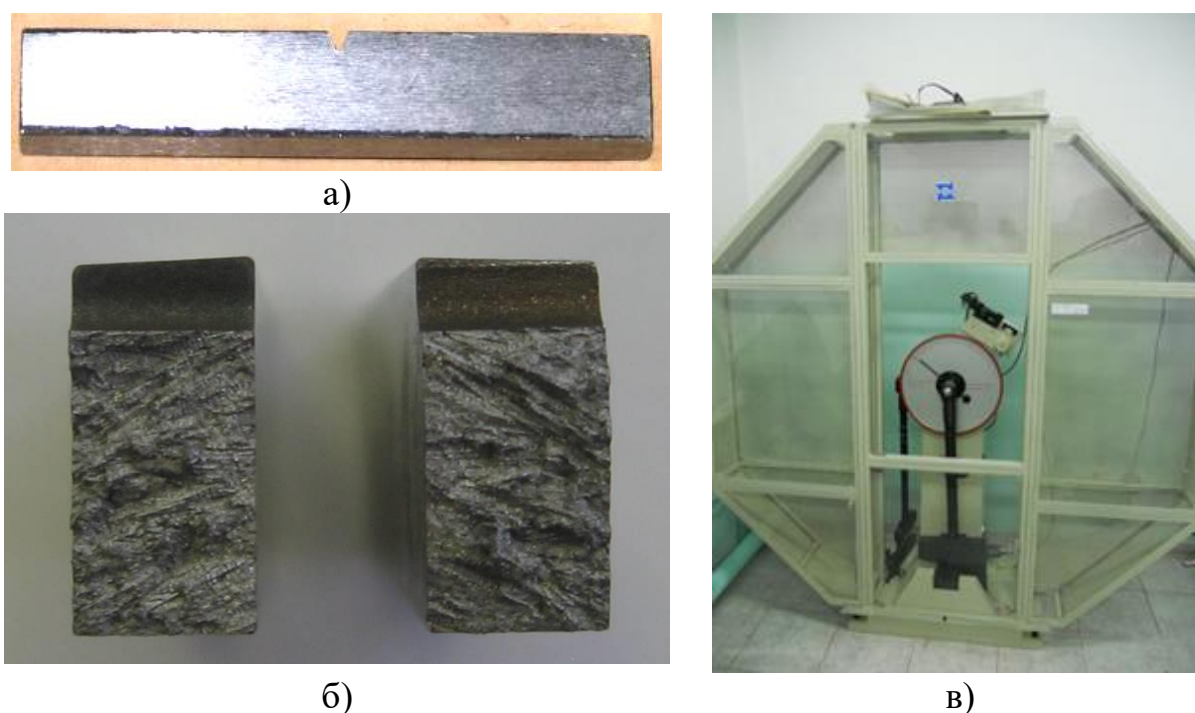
Вид образца до испытаний (а); вид изломов после испытаний (б); маятниковый копер марки JB-W300 (в)
